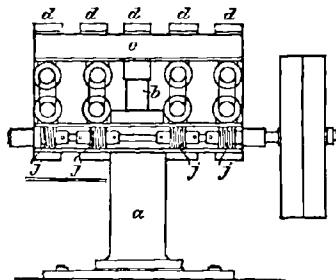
Machine à merceriser de Thomas et Prévost; vue antérieure.
